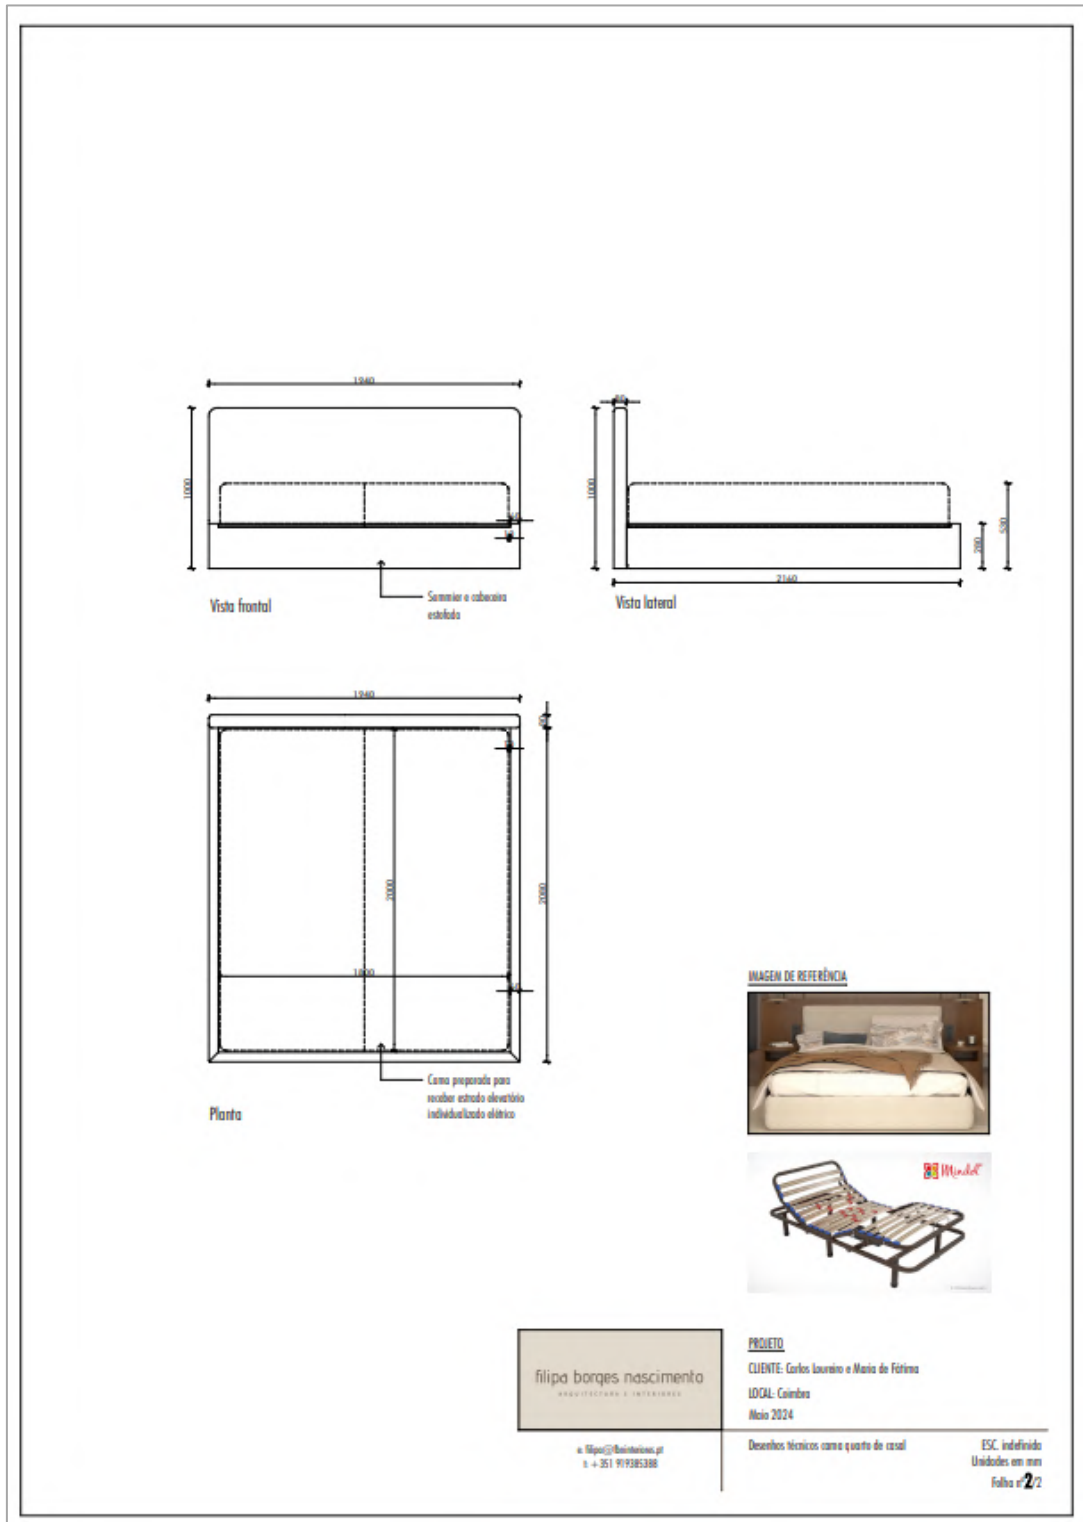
Desenho técnico cama de casal suite master - Projeto CLM. Fonte: Autora.
